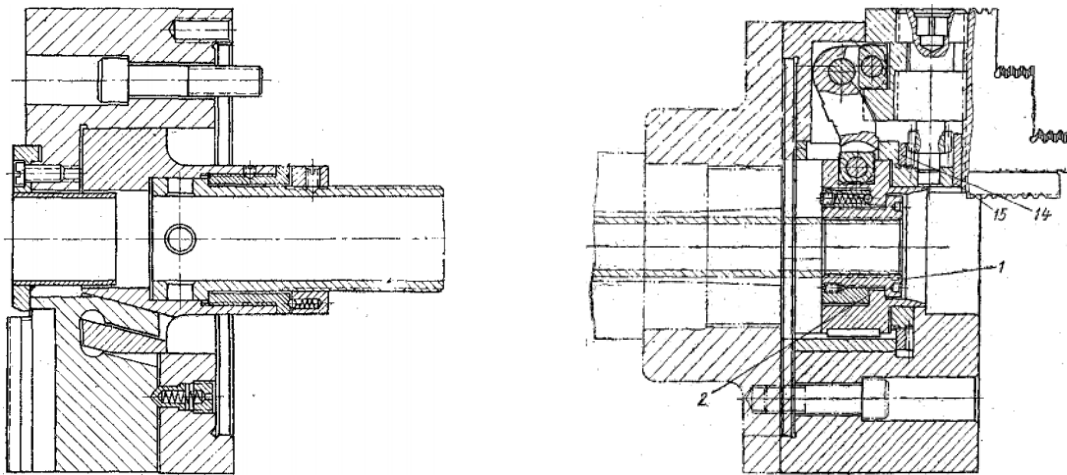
Трехкулачковый клиновой патрон, позволяющий обрабатывать прутковый материал
